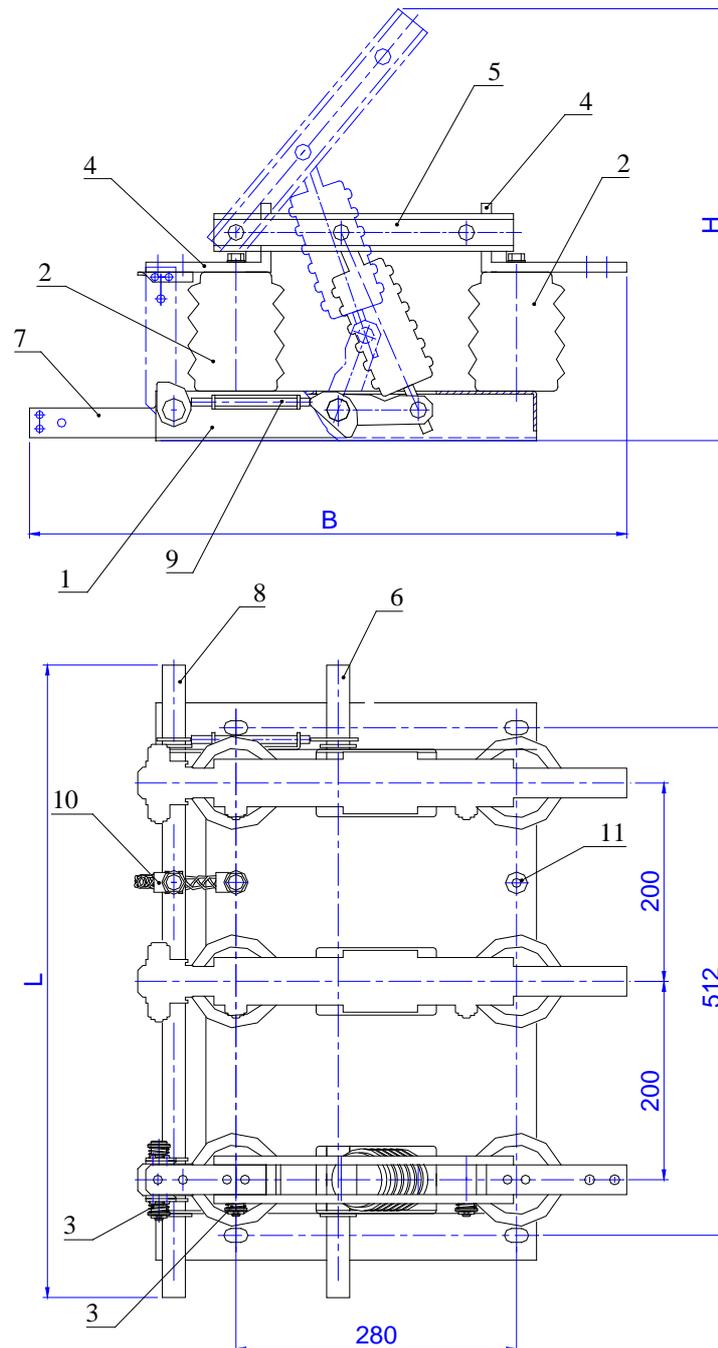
Разъединитель типа РВ3. 1- изолятор опорный; 3- пружина поджатия; 4- неподвижный контакт; 5- подвижный контактный нож; 6- вал разъединителя; 7- заземляющие ножи; 8- вал заземляющих ножей; 9- блокировка; 10- гибкая связь; 11- площадка заземления.
